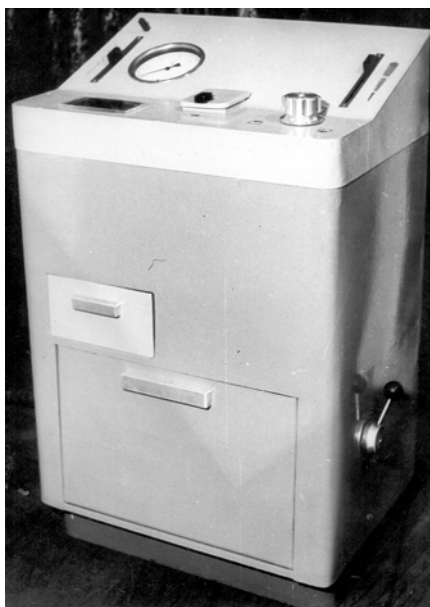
Схема установки для абразивної обробки деталей затопленими струменями
